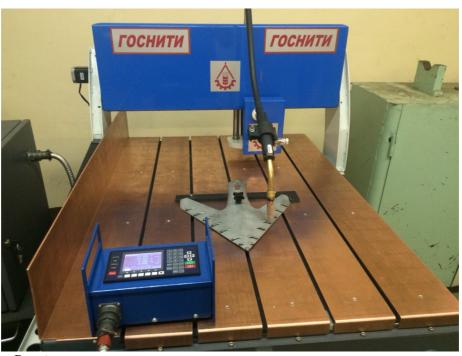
Установка для упрочнения деталей электродуговой наплавкой
